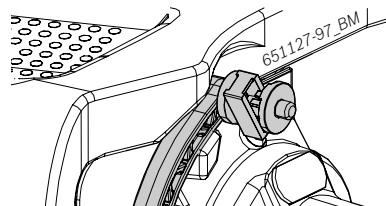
Elektronischer Messschieber zur Befestigung der Klebegewichte
